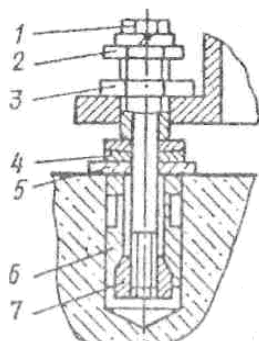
Установка оборудования на винтовых опорах с цанговым креплением:
